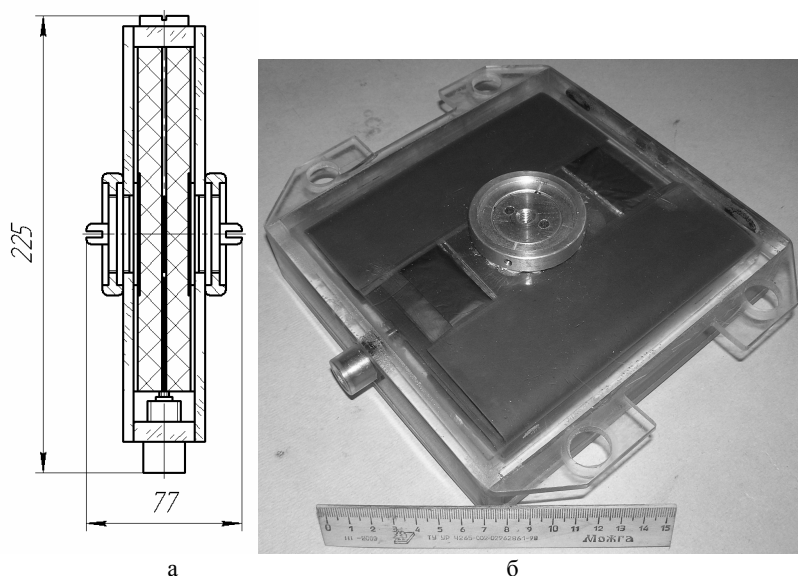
Конденсатор КИМ-131: а – габаритные размеры, б – внешний вид
